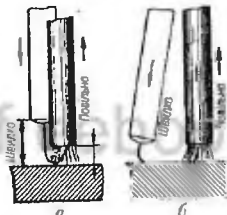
Способи запалювання зварювальної дуги: а — впритул; б — широким
